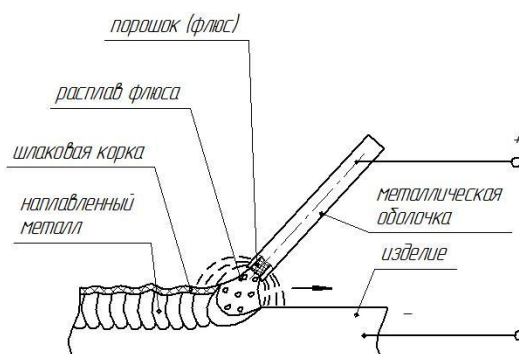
Схема осуществления сварки самозащитной порошковой проволокой
